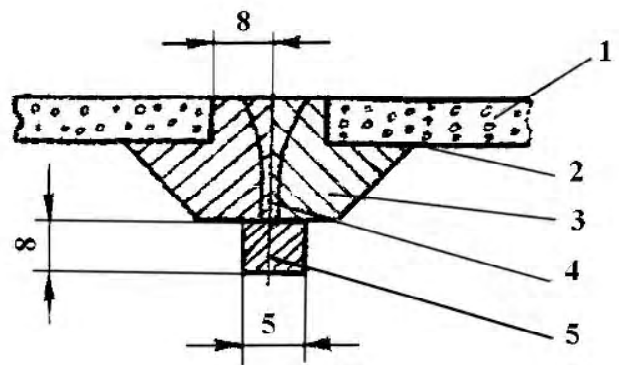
Схема зварного вузла, який зібрано під електроннопроменеве зварювання бороволокнистих труб:
